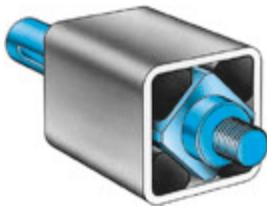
Innenvierkant aus Vollmaterial mit beidseitig angedrehten Anschlüssen
